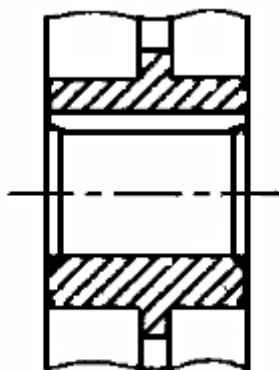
Посадочное отверстие шкива – цилиндрическое со шпонкой.
